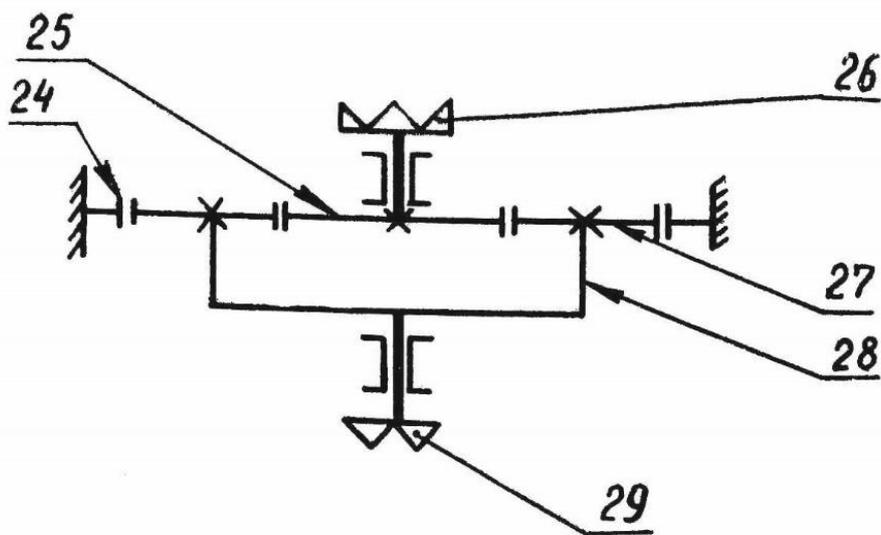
Кинематическая схема дополнительного редуктора привода типа Д
